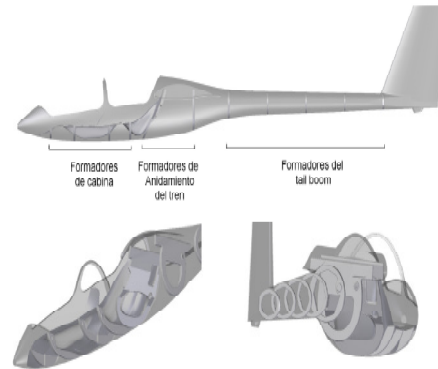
Vista General de la Estructura Dentro del Planeador.^[65]
